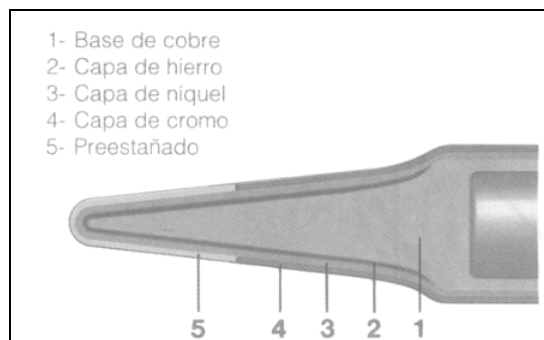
Capas protectoras de una punta de un soldador.
